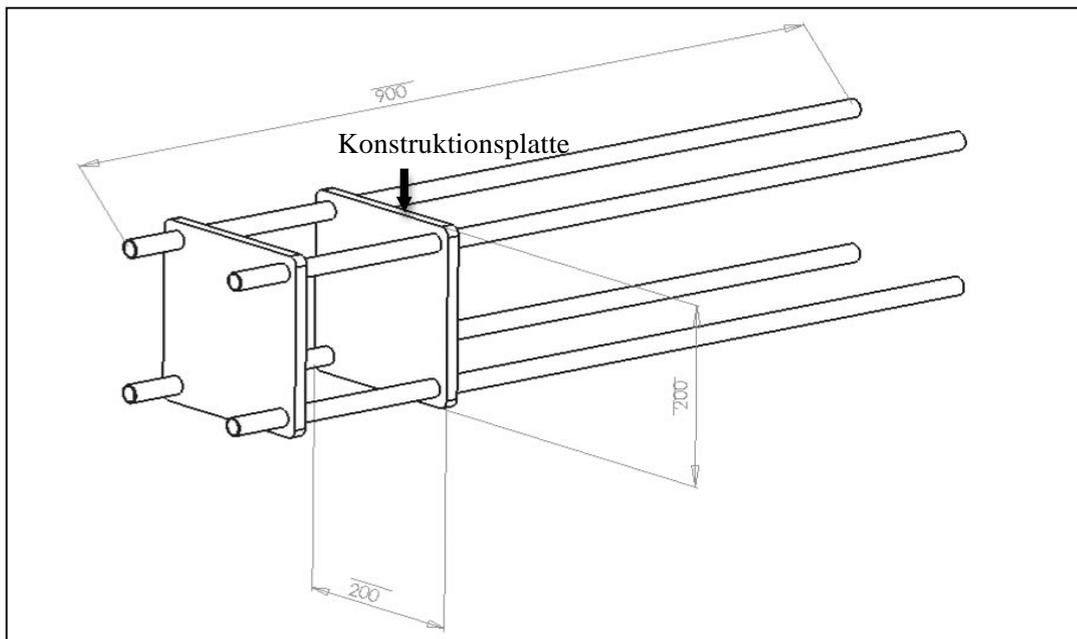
Gerüst aus vier Stangen mit zwei aufgesteckten Konstruktionsplatten (Maße in mm).
